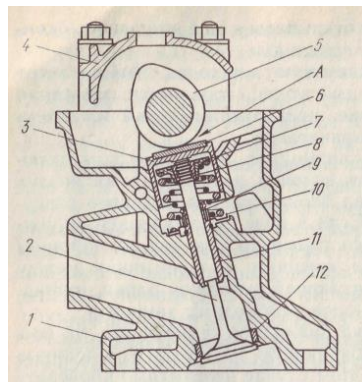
Розріз головки циліндрів двигуна автомобіля ВАЗ-21093 по впускному клапану:
